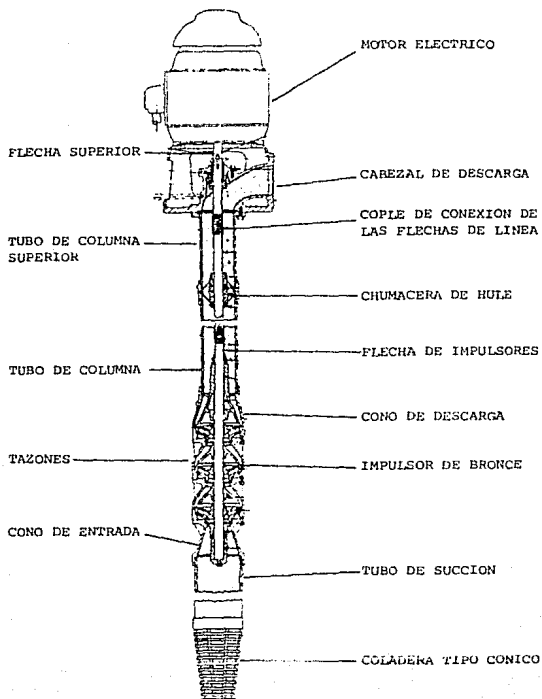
CONJUNTO BOMBA-MOTOR PARA POZO PROFUNDO
